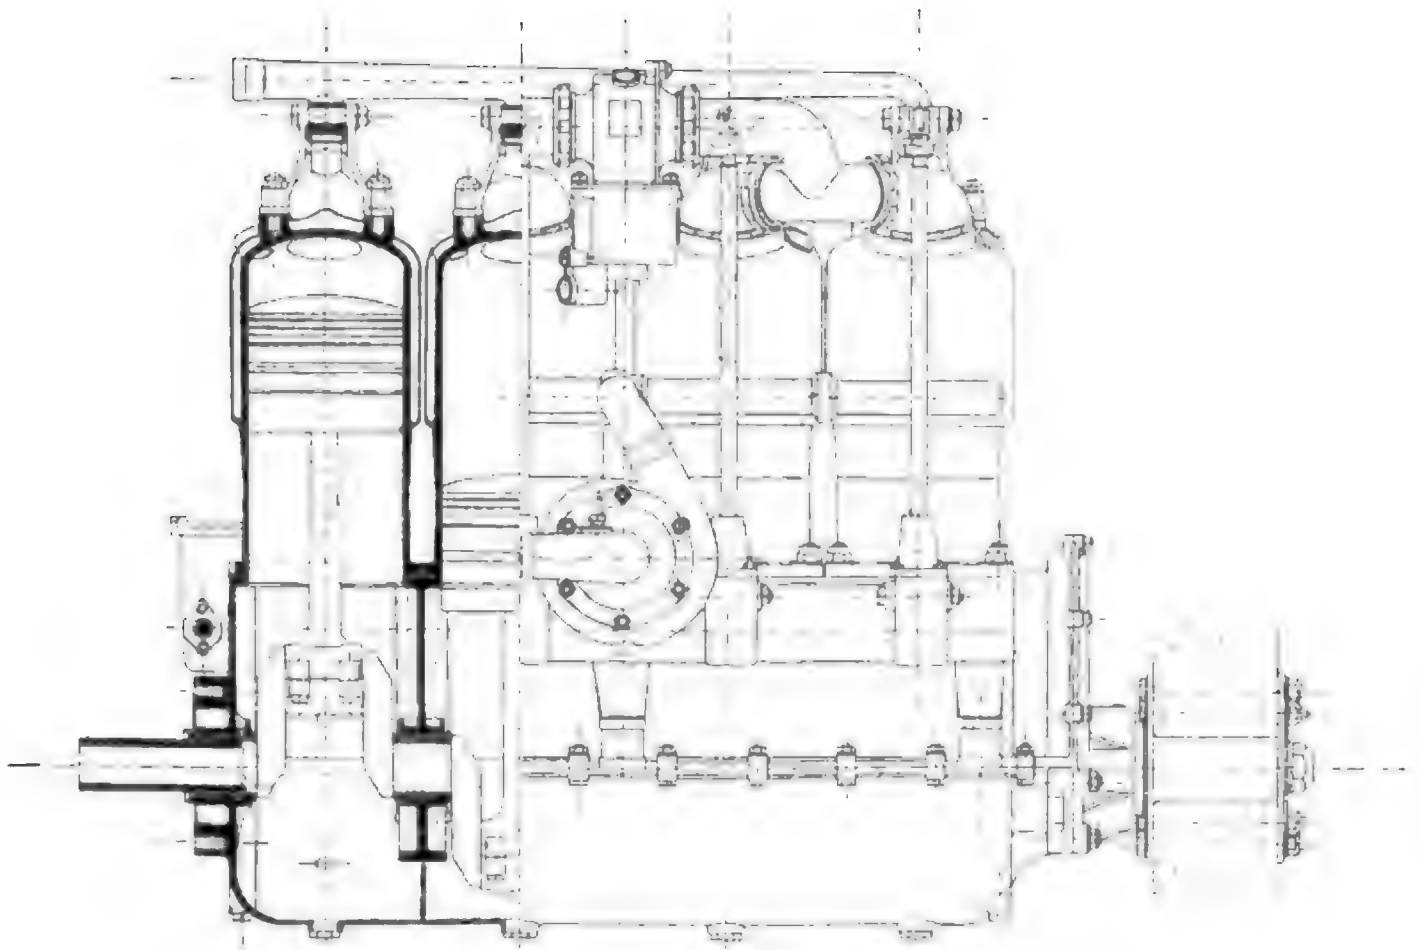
Flugmotor der Österreichischen Daimler-Werke, Längsschnitt und Seitenansicht.
